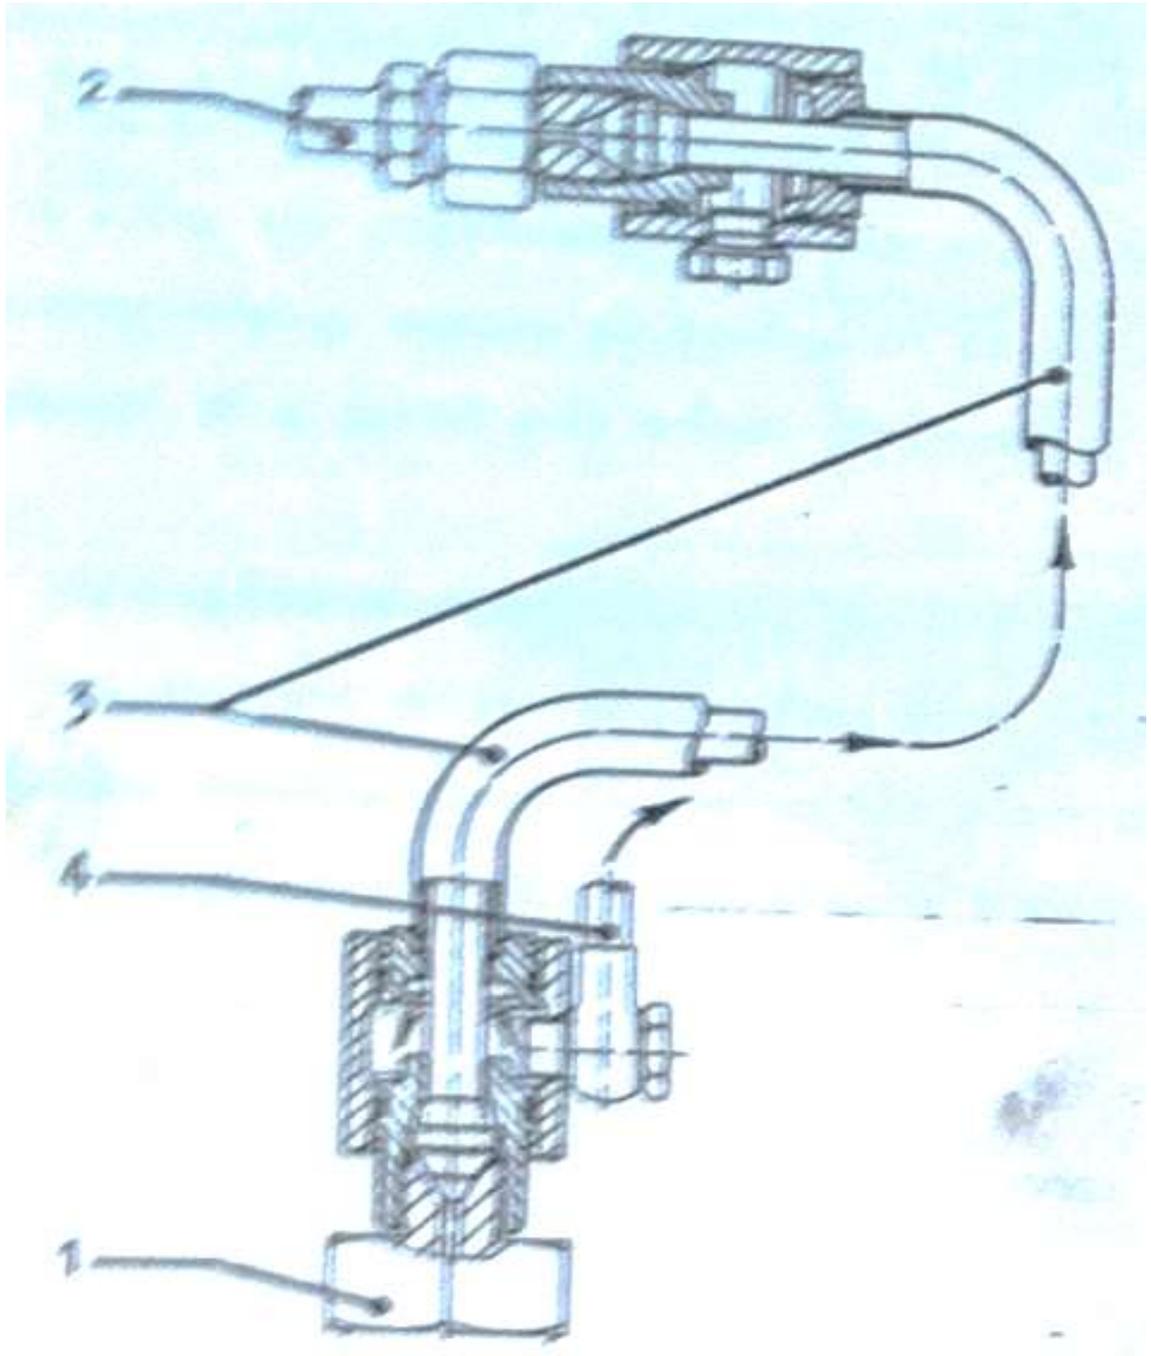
Tubería de inyección. Fuente: Elaboración propia.
